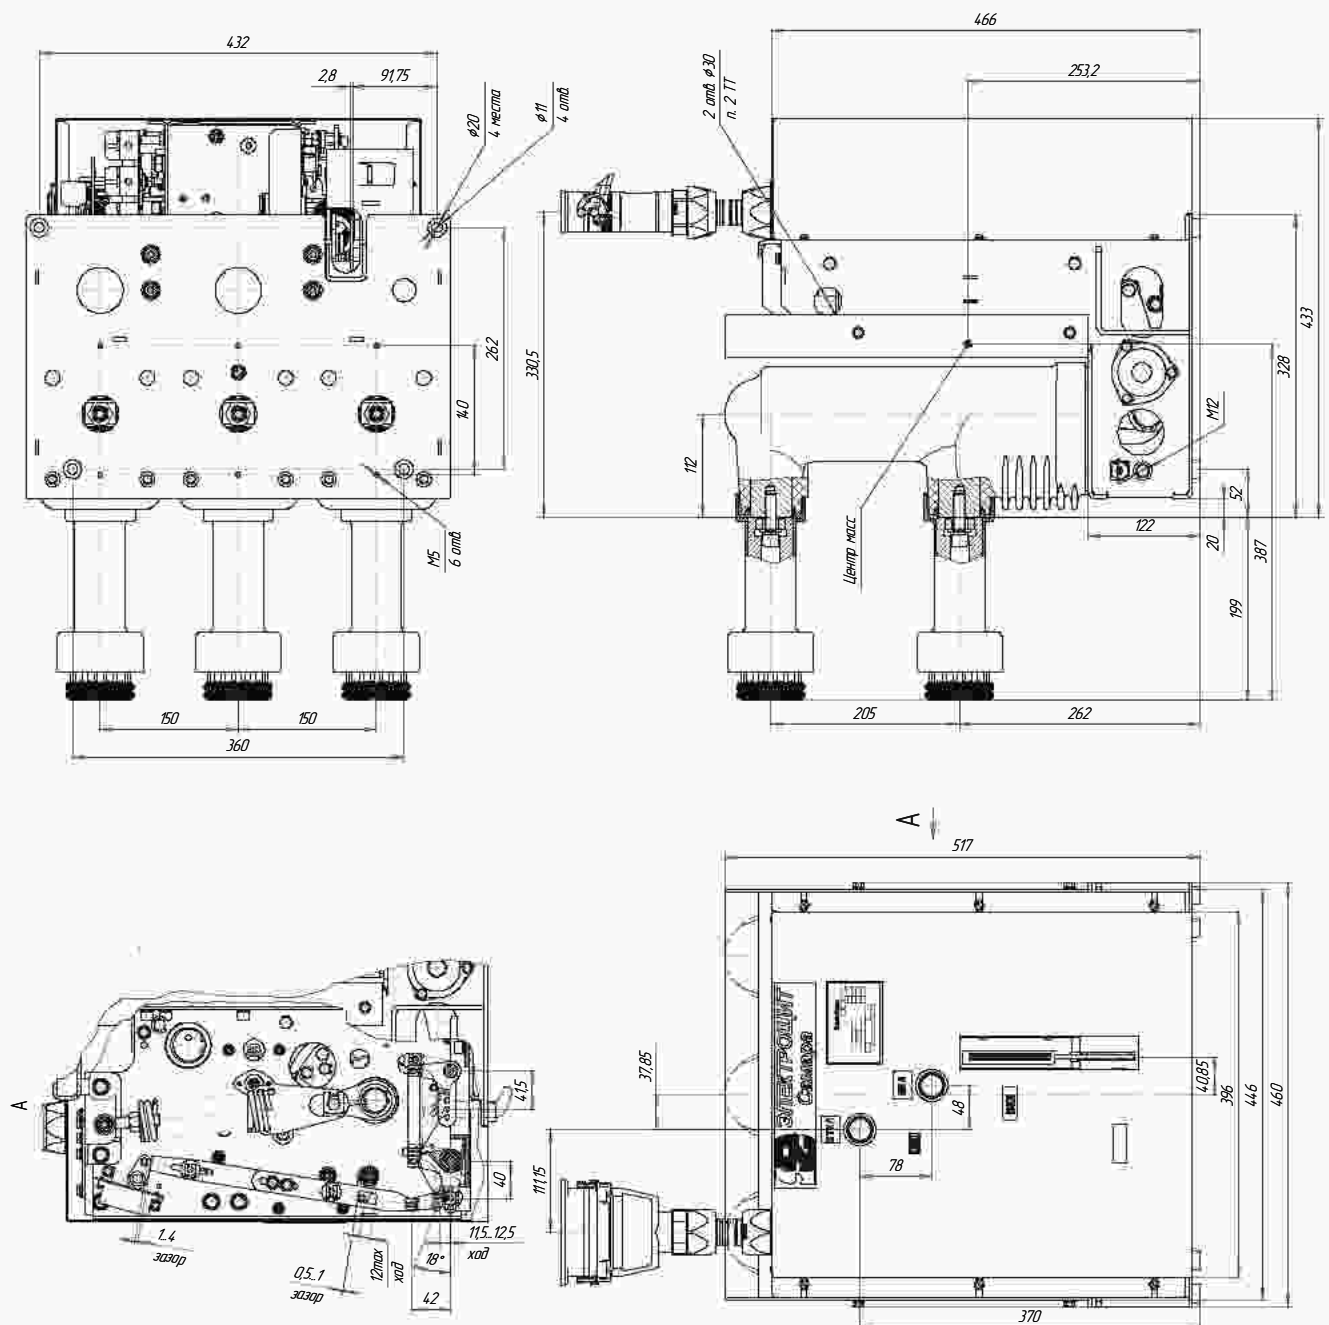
Габаритные, присоединительные и установочные размеры выключателя типа ВВУ-СЭЦ-П-10-25/1250
